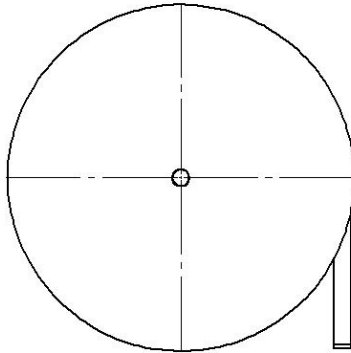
2D-модель разрабатываемой конструкции. Вид сверху
